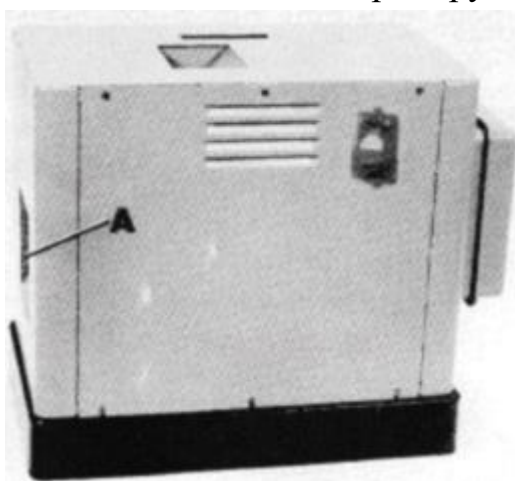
Расположение разгрузочного лотка и лотка для сбора стружки
